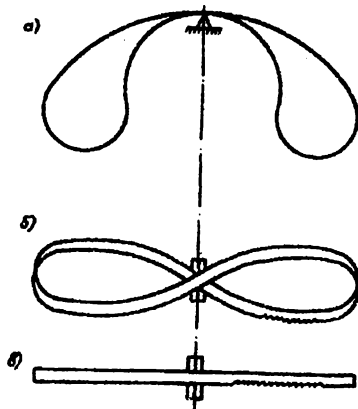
Схема проверки правильности сварки концов полотна ленточной пилы
